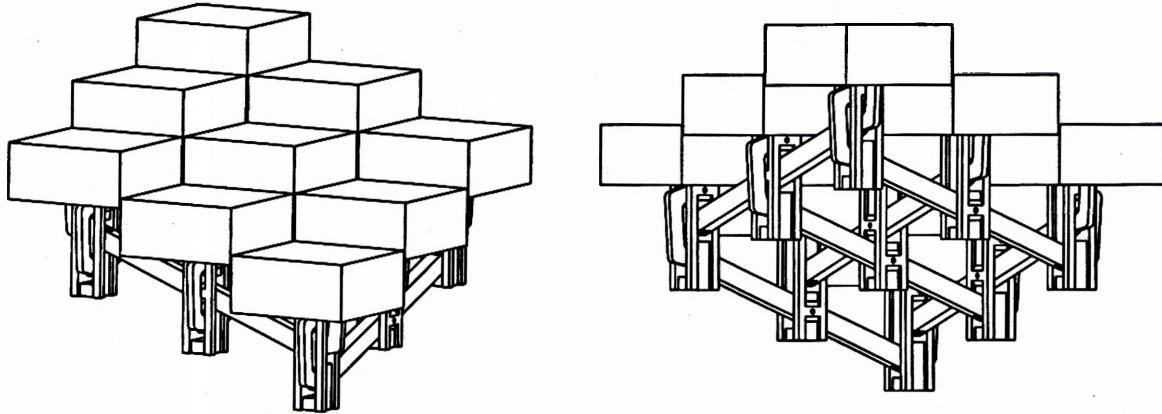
Illustrations de l'assemblage des plateaux mobiles et des mécanismes de moyennage du prototype.
